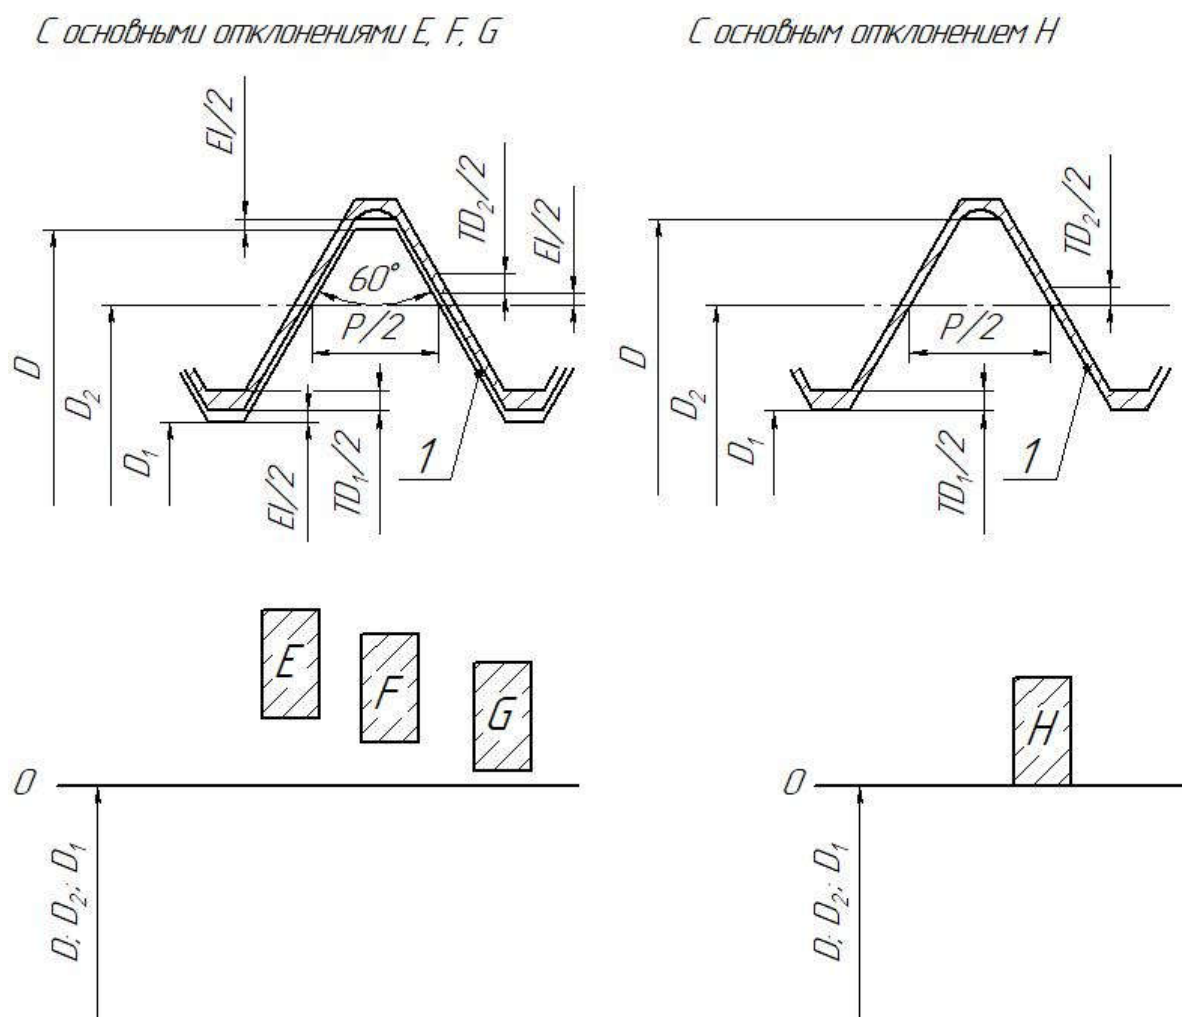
Схема положения интервалов допусков внутренней резьбы по [6]:
